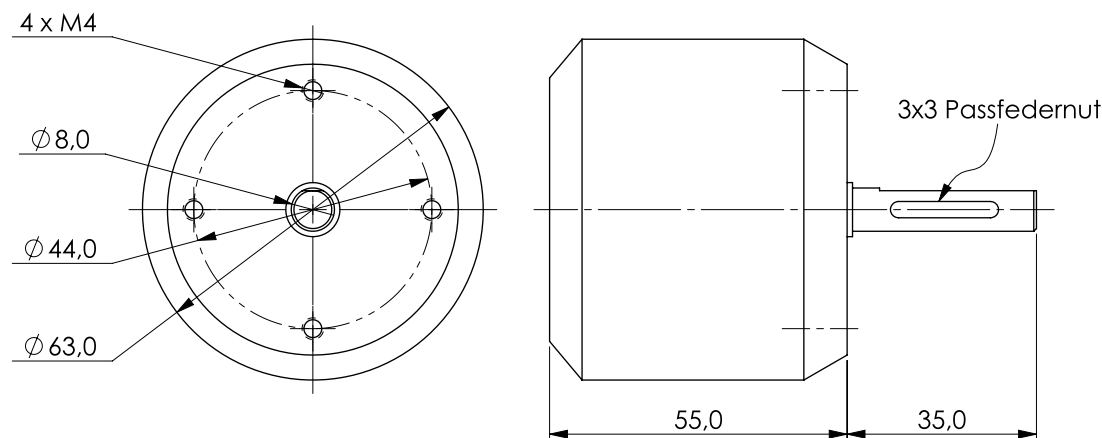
Relevante Dimensionen des Motors *TorqueBoards 6355 190KV*.
